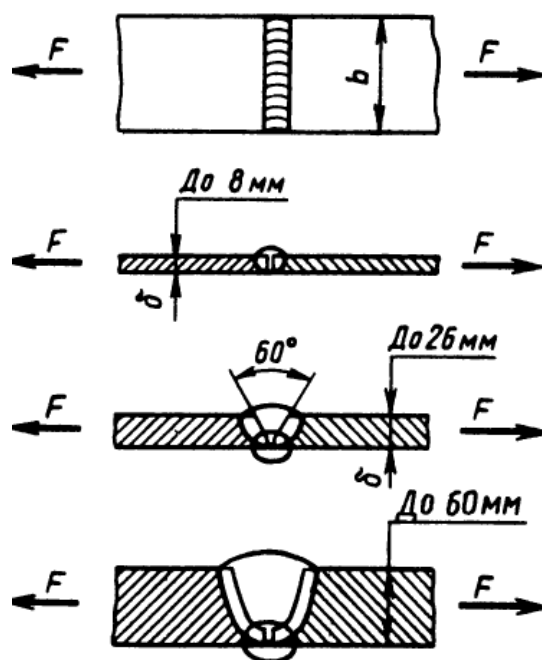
Стыковое сварное соединение разной толщины
